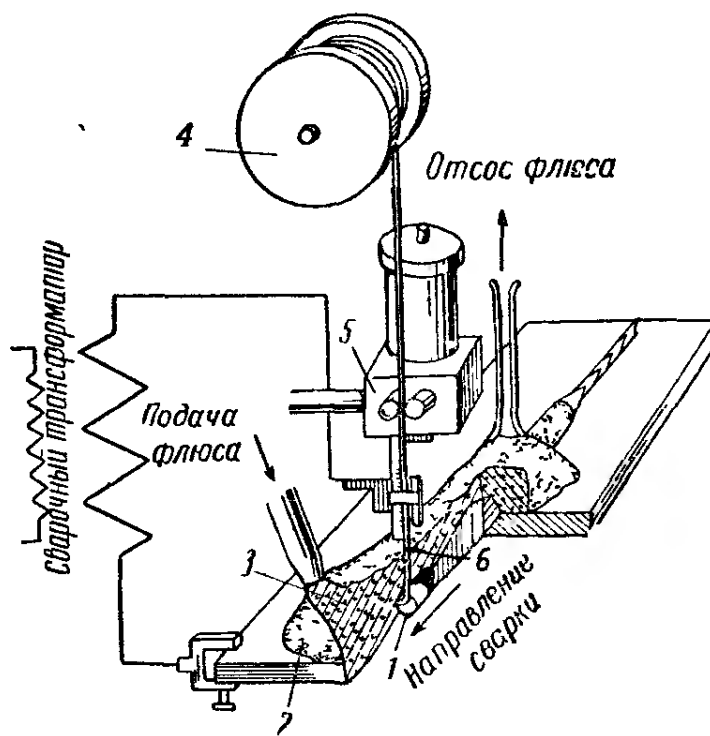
Схема процесса автоматической сварки под флюсом
